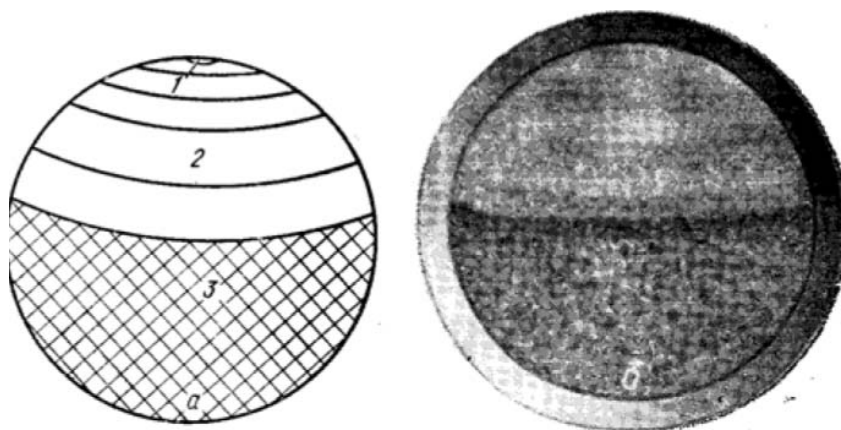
Усталостный излом: а – схема макроскопического излома; б – одноочаговый усталостный излом; 1 – фокус излома; 2 – область постепенного распространения трещины с линиями усталости; 3 – зона долома
